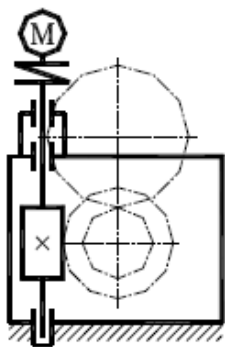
Схема № 0 – Привод, состоящий из червячного редуктора и цилиндрической открытой передачи
